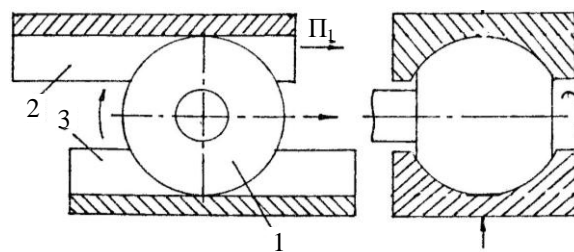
Схема способа полноконтактной обкатки сферической поверхности
